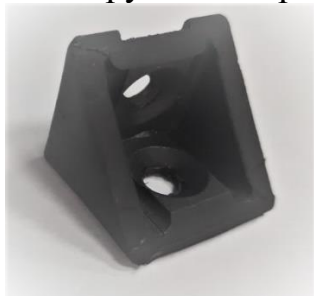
Внешний вид уголка для крепления корпуса спутника
